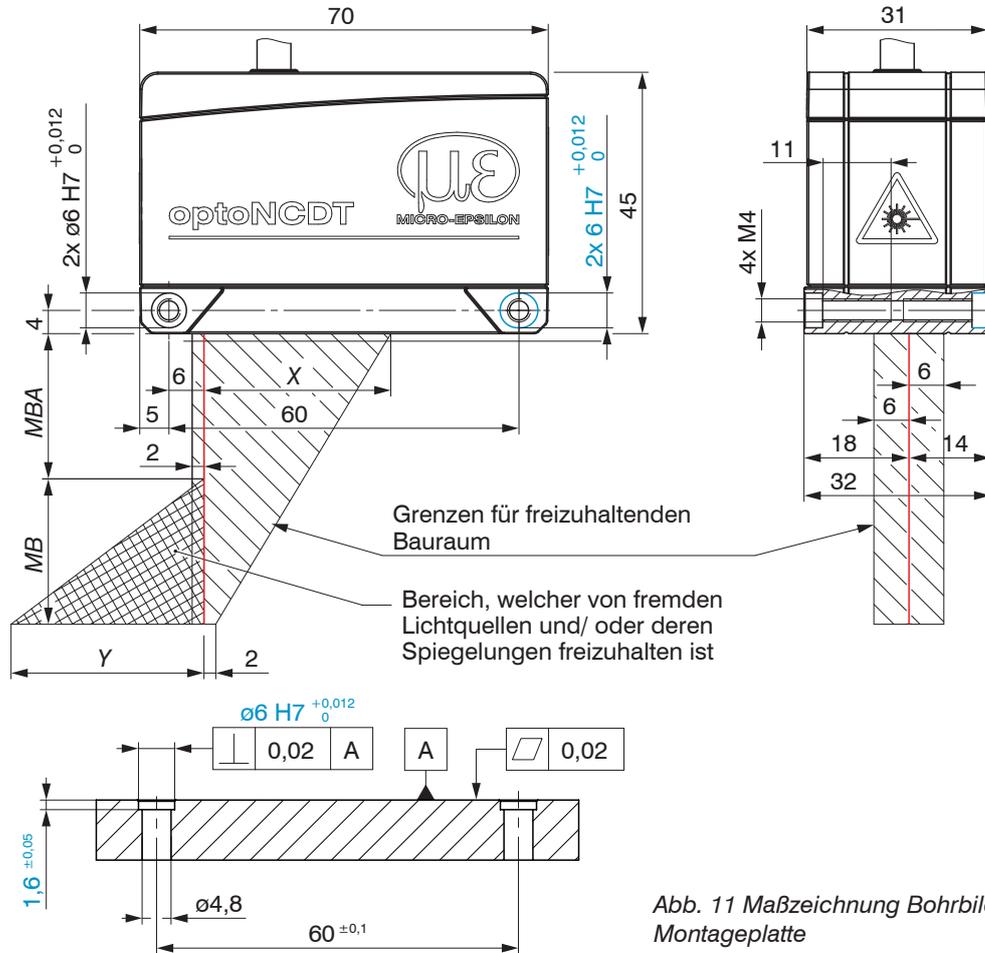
Maßzeichnung Bohrbild Montageplatte
